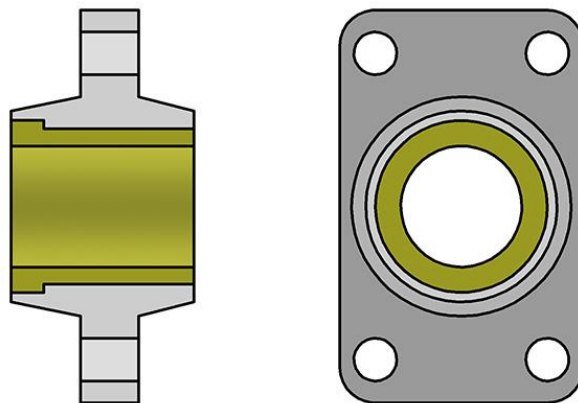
Конструкція нероз'ємного підшипника ковзання
